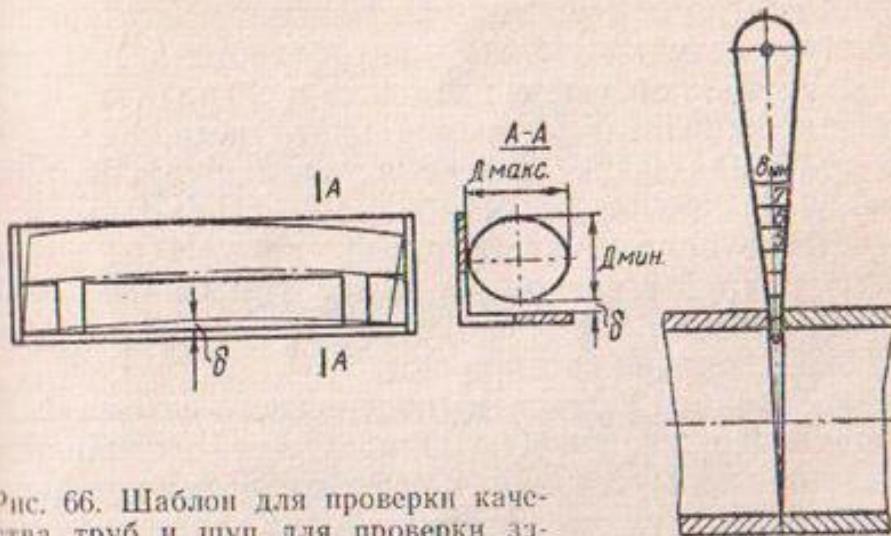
Шаблон для проверки качества труб и щуп для проверки зазора в стыке.
